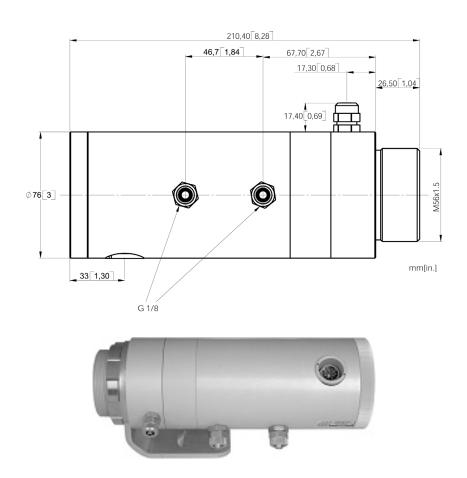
Messkopf mit luft-/wassergekühltem Gehäuse
